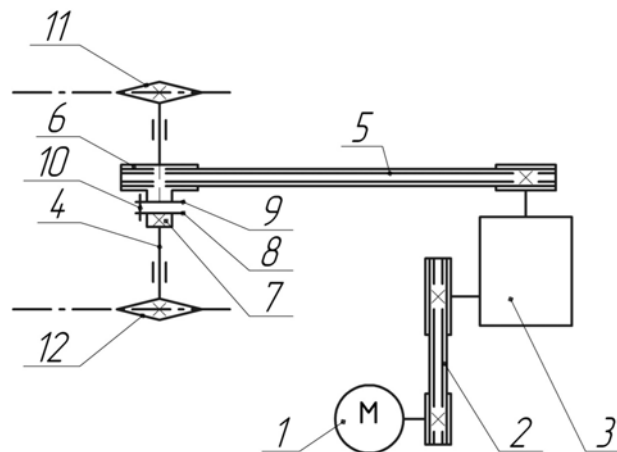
Кінематична схема привода рукавичного автомата з запобіжною муфтою
